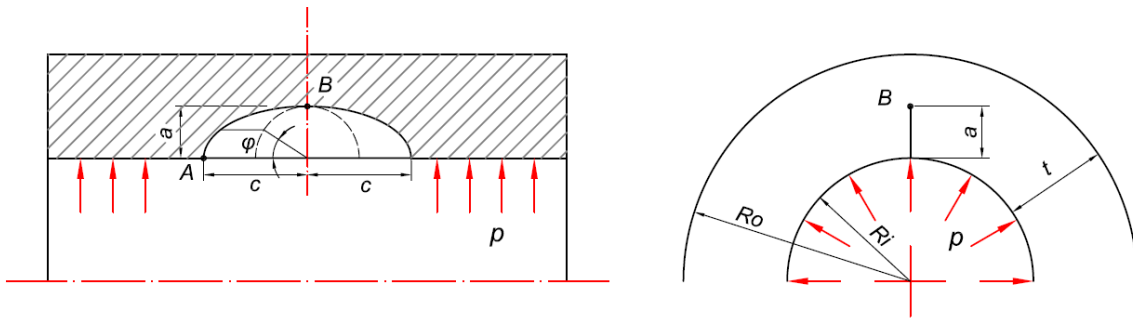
Tubería con fisura semi-elíptica interna en dirección axial sometida a presión interna.
